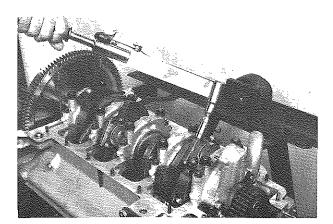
Biella del cilindro 8 Cylinder 8 con-rod
